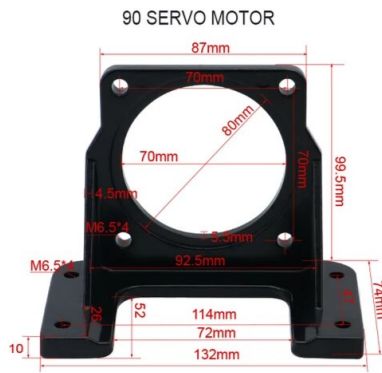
Soporte para el motor , Fuente: Aliexpress
